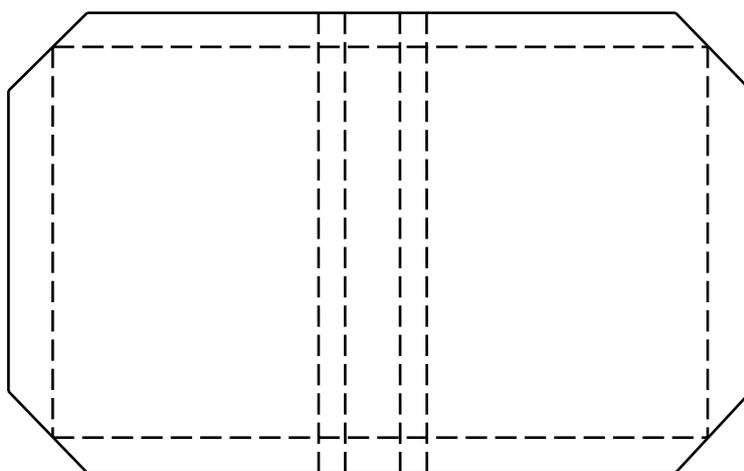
Вид заготовки для интегральной переплетной крышки
